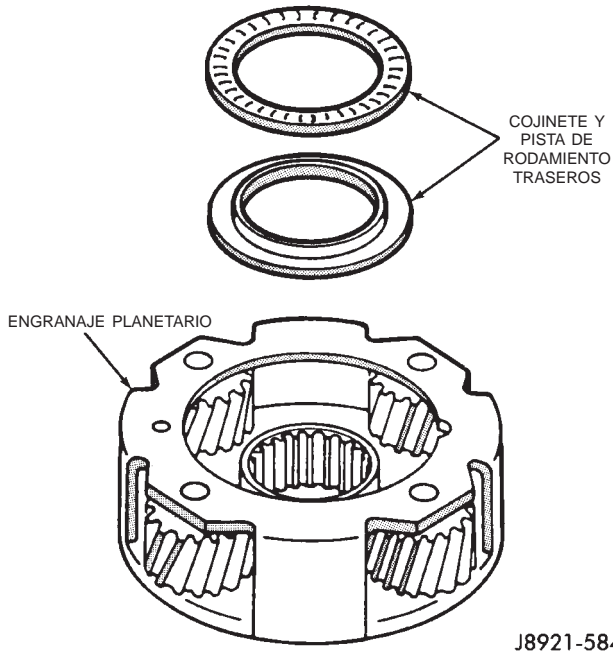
Instalación del cojinete y la pista de rodamiento traseros del engranaje planetario delantero
